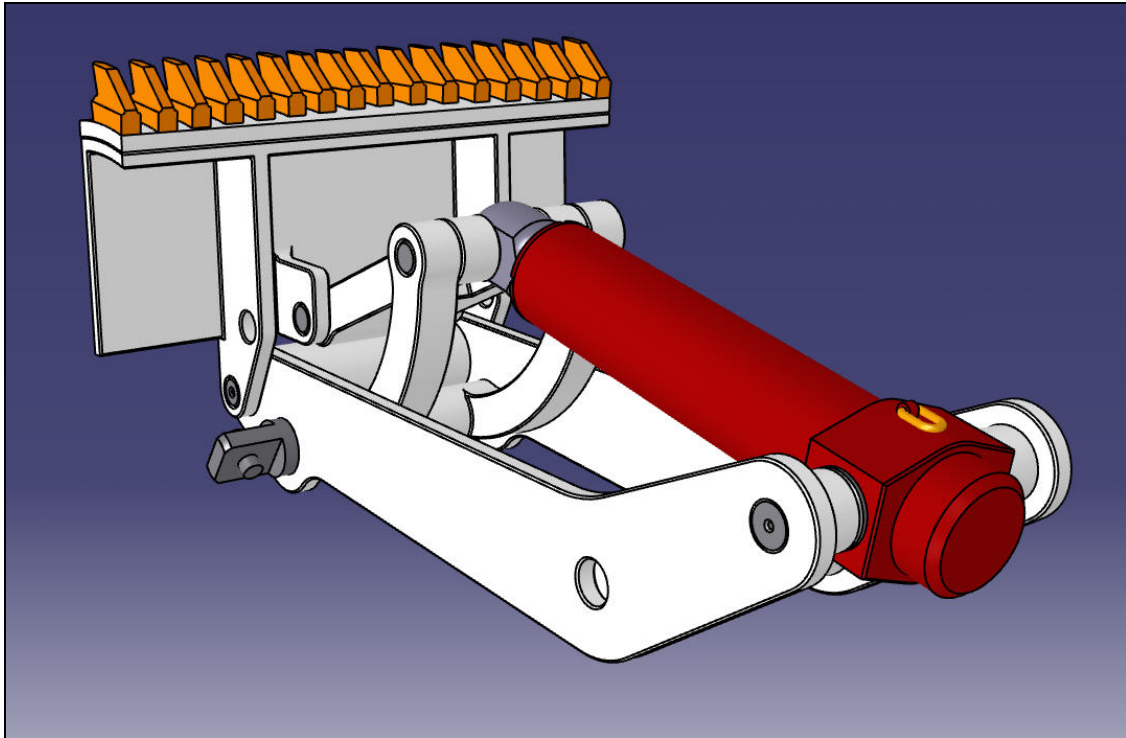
Kernbaugruppen der Gewinnungseinrichtung
